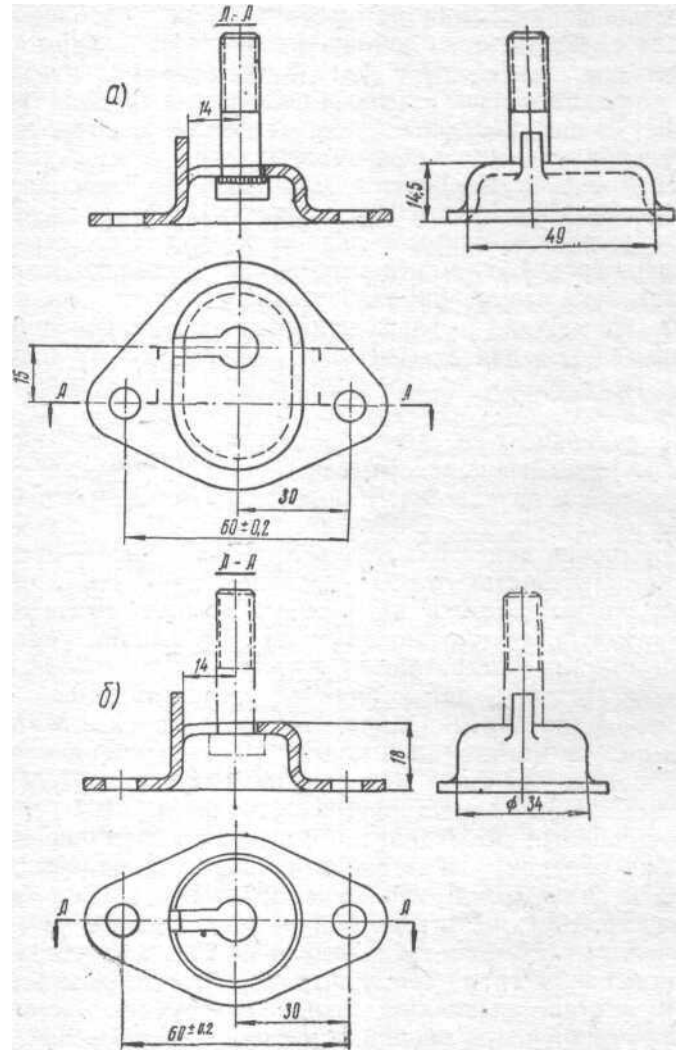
Переходные детали узла крепления передних опор двигателя:
